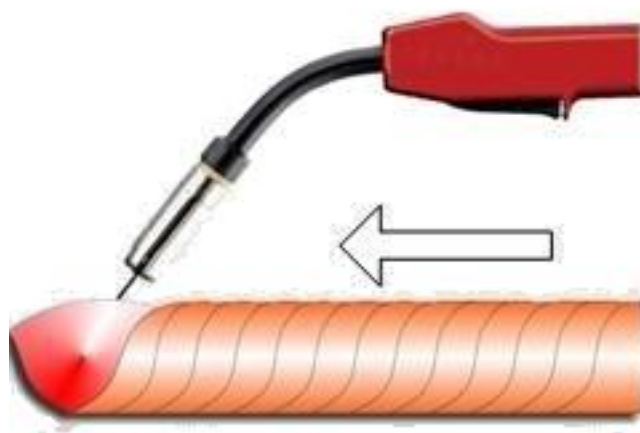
Схема процесса механизированной сварки углом вперед
